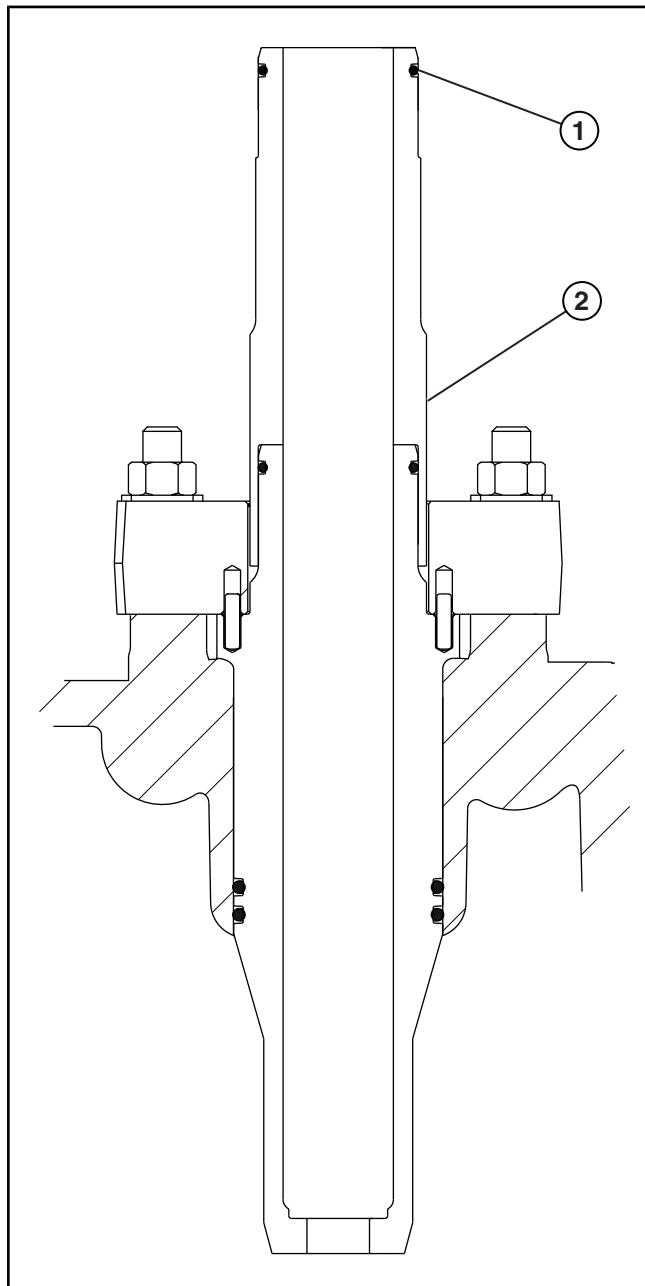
Установка удлинителя свечи зажигания
